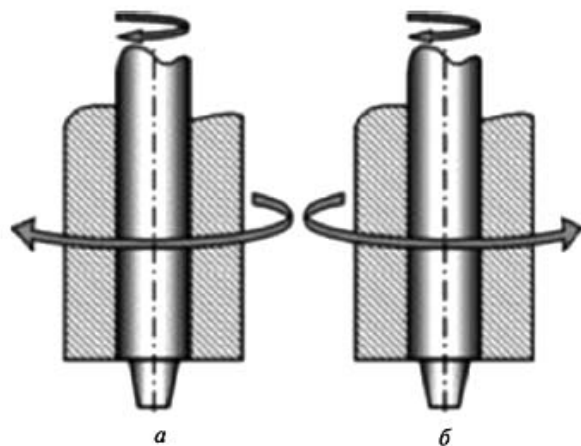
Инструменты с наружной и внутренней частями, вращающимися в одном (*a*) и противоположных (*б*) направлениях. Показан «намазанный» на выступ свариваемый металл
